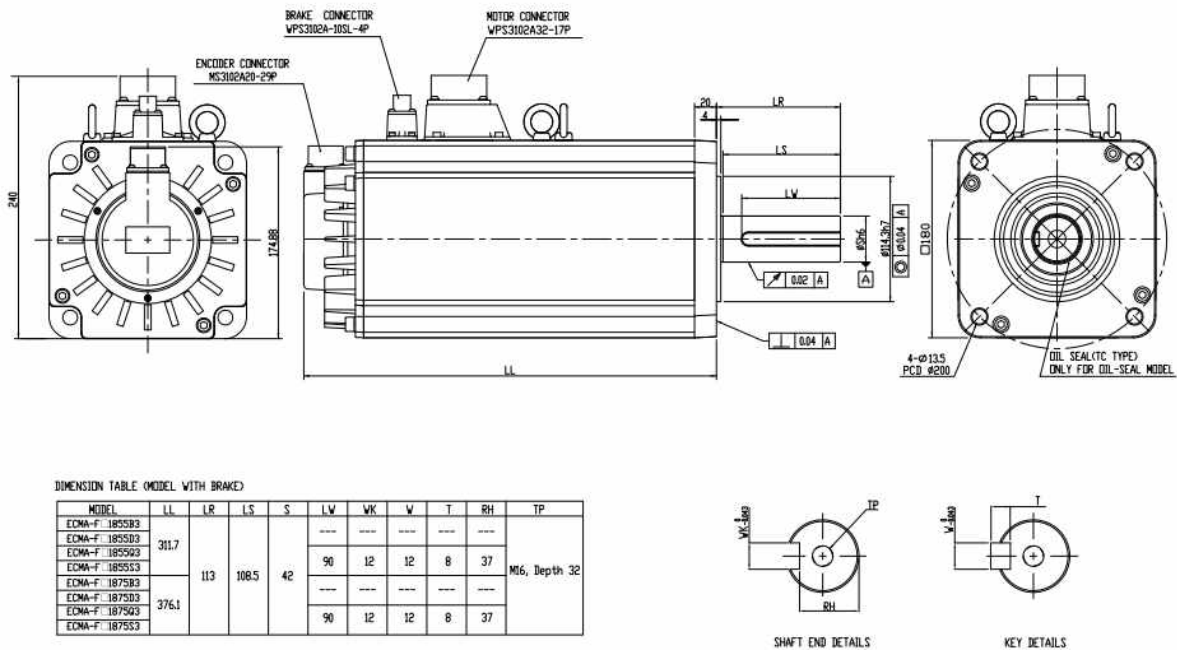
Desenho técnico do servo motor DELTA ECMA
